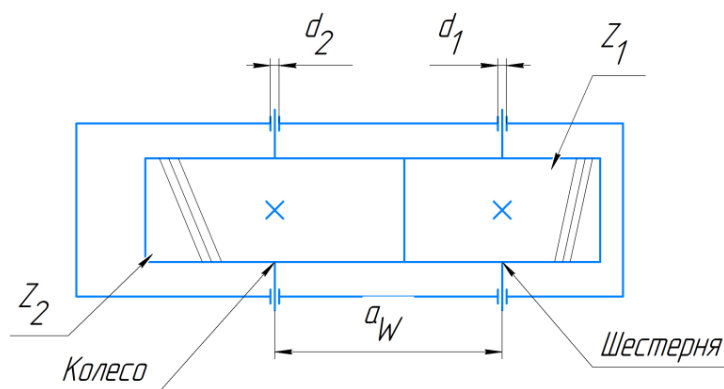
Схема цилиндрической прямозубой передачи редуктора
